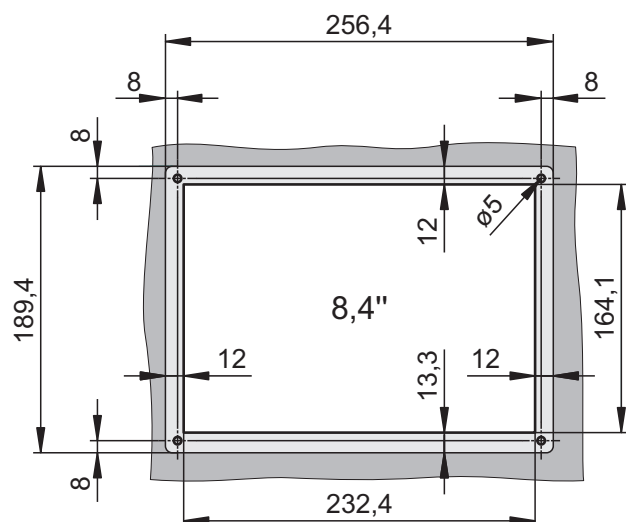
Plan de perçage écran tactile 8,4 " (vue de face de l'appareil, toutes les dimensions en mm)
